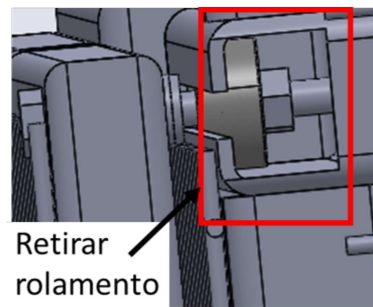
Detalhes de construção mecânica - Colocação e retirada do rolamento
